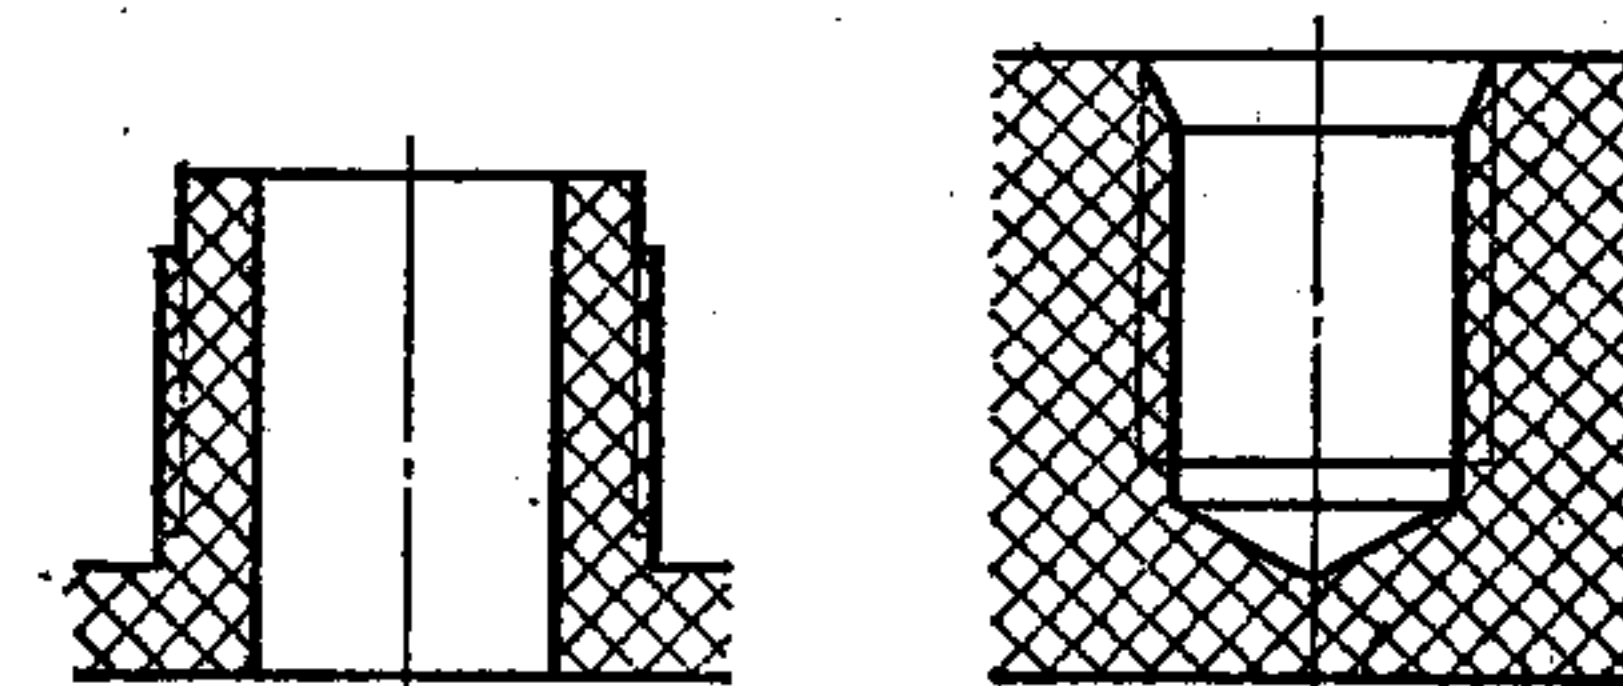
Крышка из пресс-материала АГ-4В с резьбой круглого профиля
